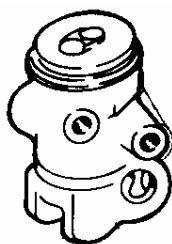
Цилиндр колесный заднего тормоза 2101-3502040-10, 2105-3502040.
